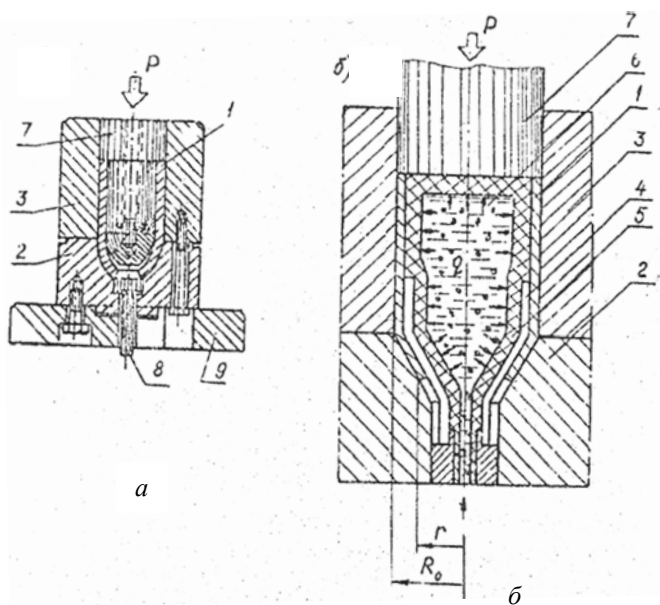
Схемы обжима с подпором по наружной (а) и по наружной и внутренней поверхностям (б): 1 – заготовка; 2 – матрица; 3 – наружный подпор; 4 – разрезная оправка; 5 – пластичный элемент; 6 – жидкость; 7 – пуансон; 8 – выталкиватель; 9 – нижняя плита
